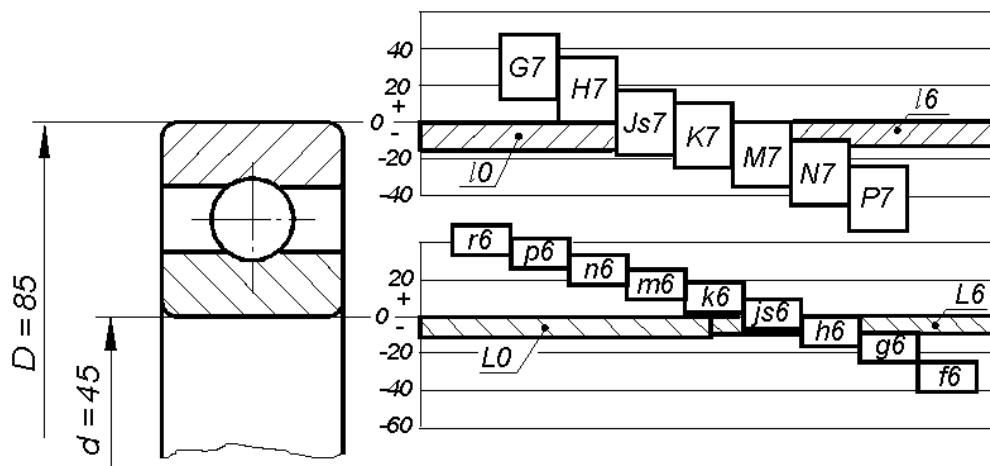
Схема расположения полей допусков посадочных диаметров подшипника и сопряженных с ним деталей для классов точности 0 и 6
